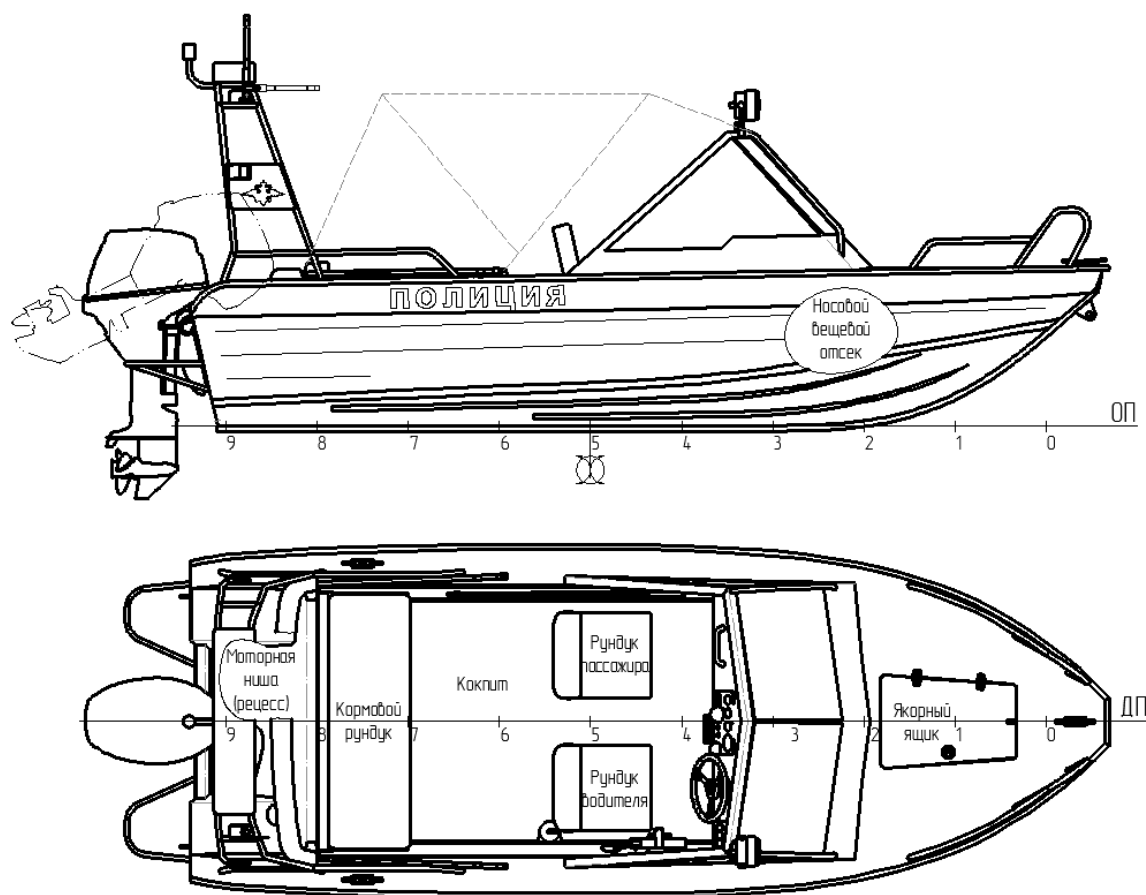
Общий вид и компоновка катера Аллигатор 46
